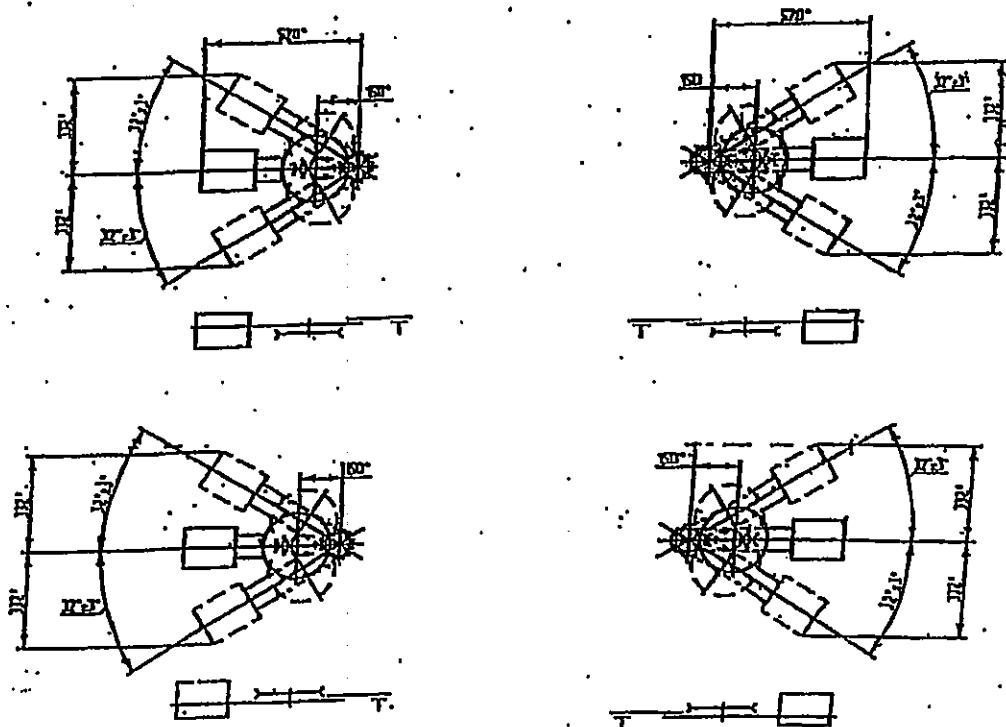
схемы сборок натяжного устройства каната ОС
